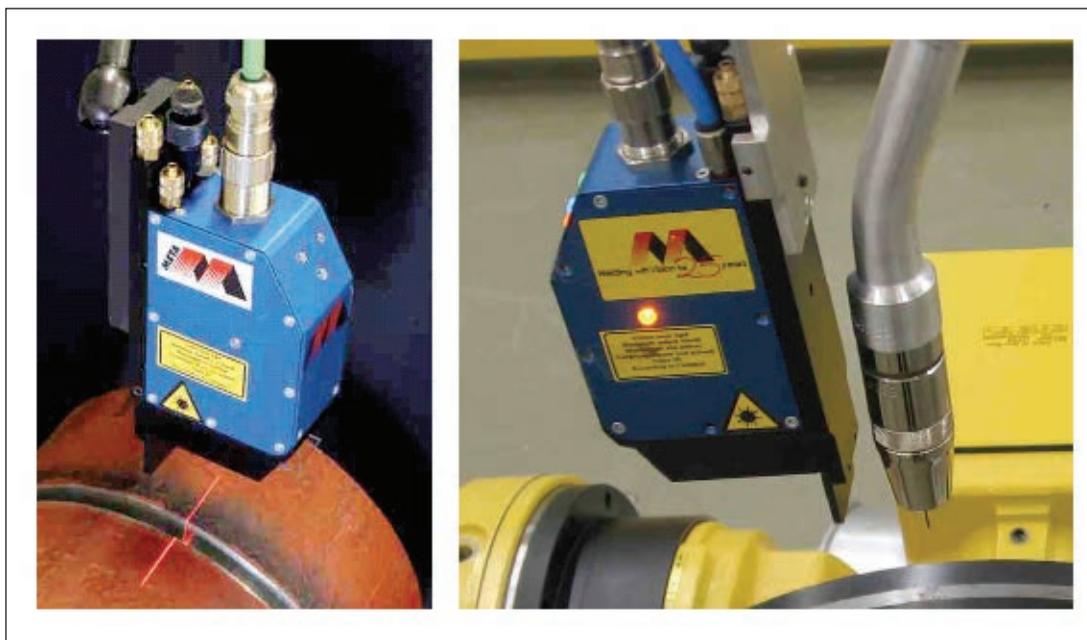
Лазерная камера METASLS-050 для слежения за осью шва, регулировки параметров сварки и возможности ее применения
